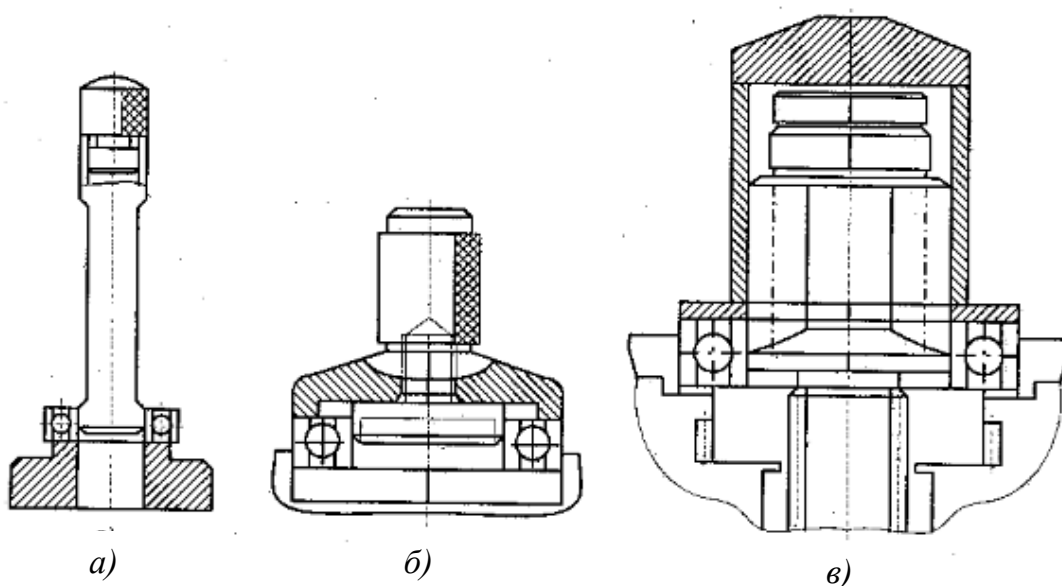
Схемы установки подшипников качения на валу и в корпусе
